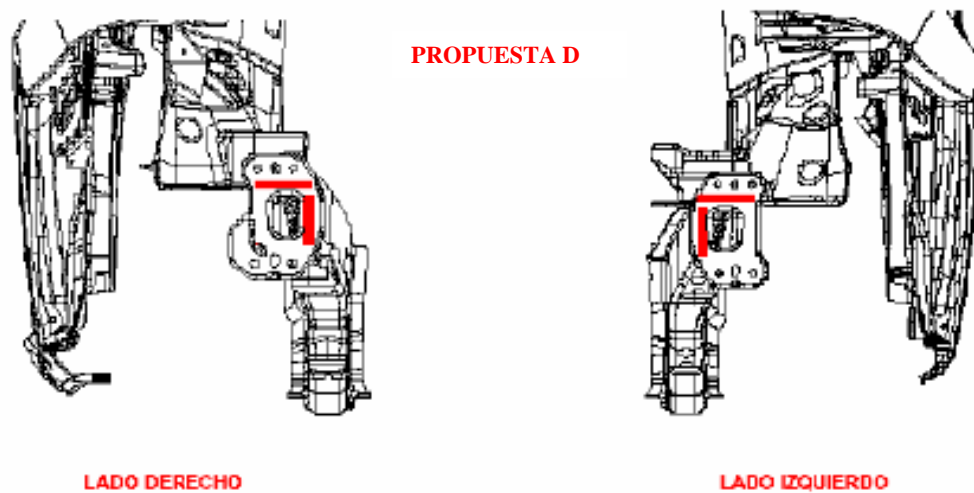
Diagrama de cordones de soldadura definitivos
